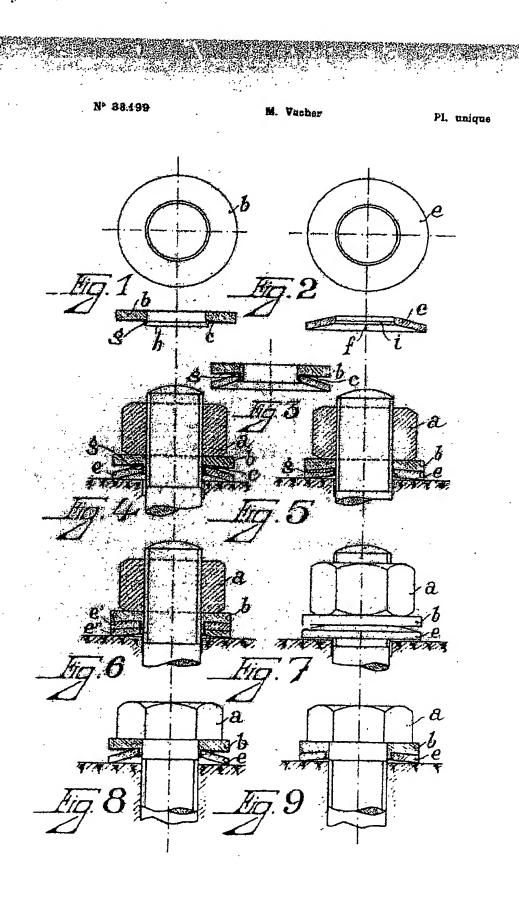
une coupe des deux rondelles assemblées par sertissage;
